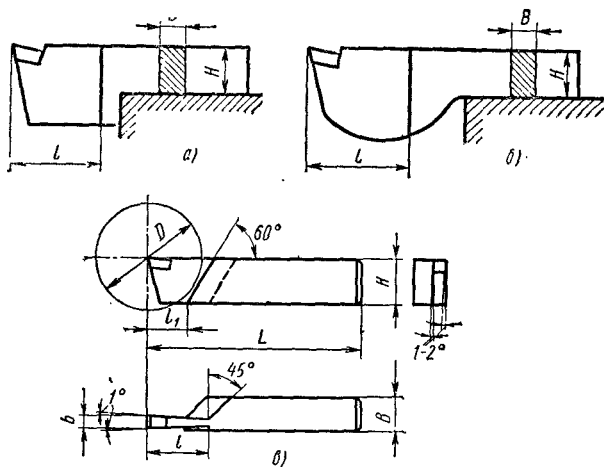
Конструкции отрезных резцов с усиленной головкой:
